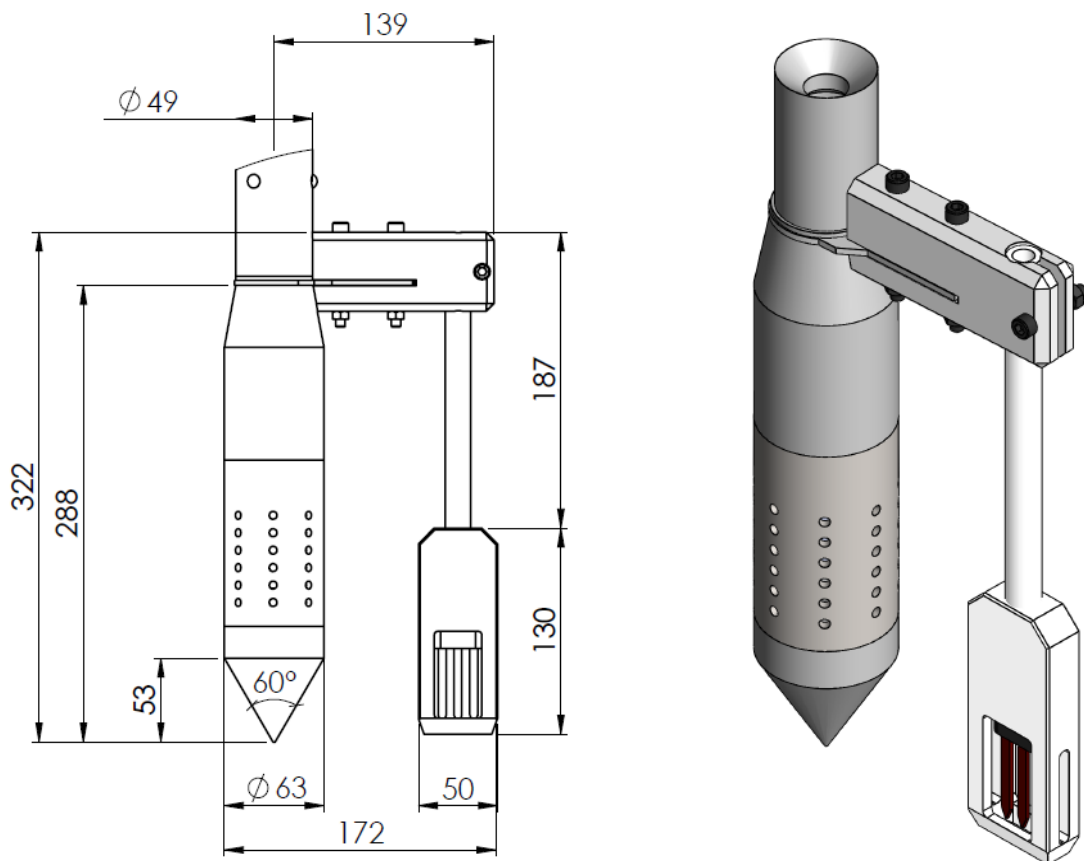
Dimensões (em mm) do suporte em náilon de proteção do sensor *5TE* acoplado à sonda-torpedo
